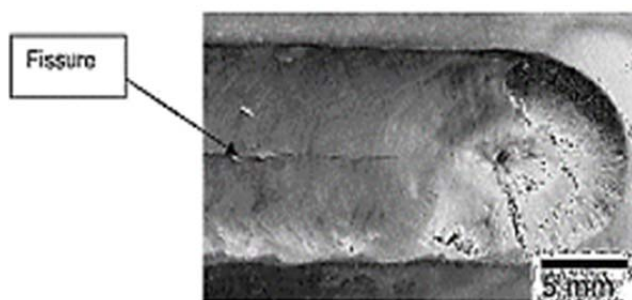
Fissure de solidification lors de soudage de l'inconel 718.
